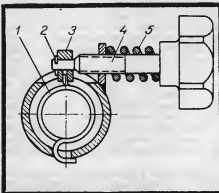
Крепление пружины демпфера: 1 — пружина демпфера; 2 — шпилька; 3 — сухарь; 4 — винт; 5 — пружина винта.
